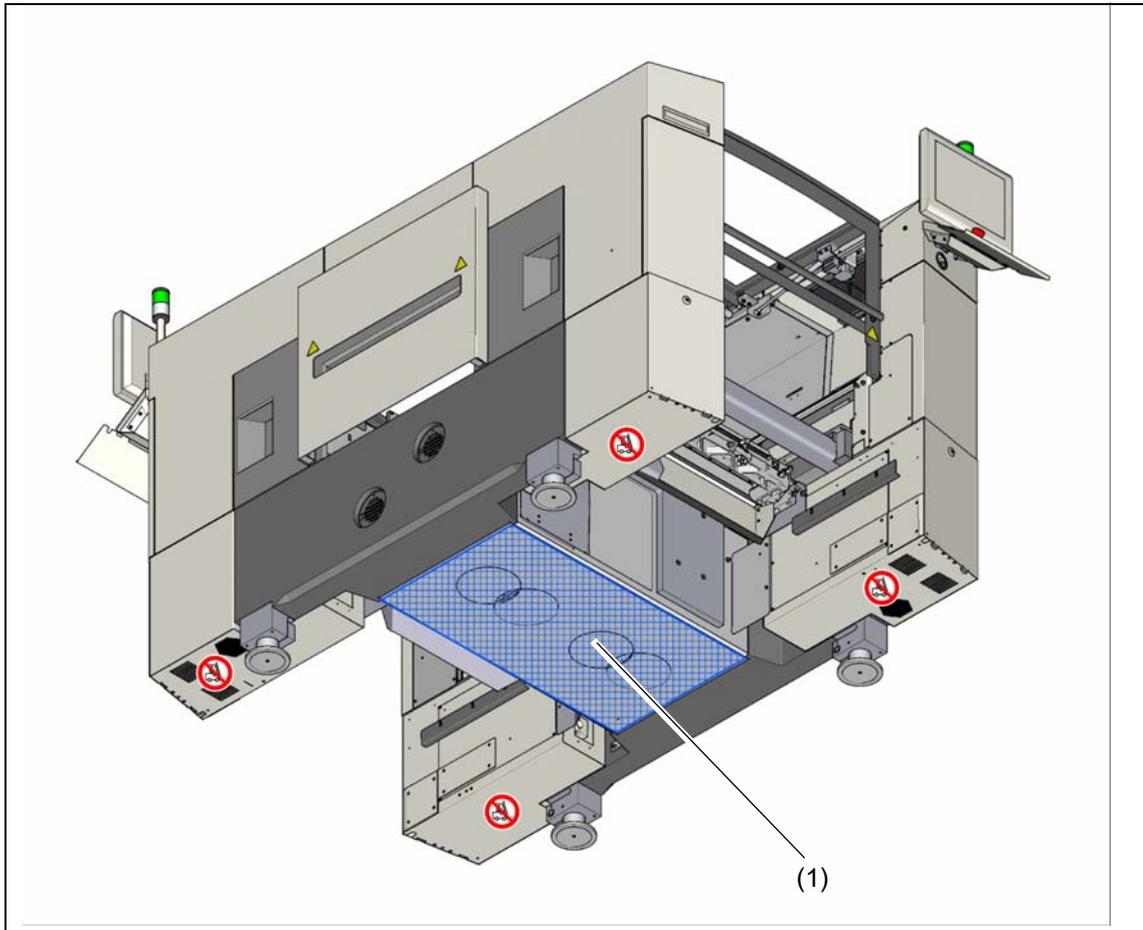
1 接触表面 - 货叉与 PCB 传送方向成直角
